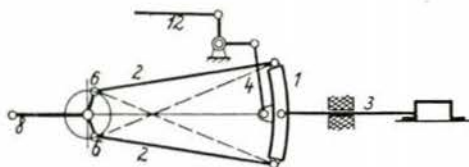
Schemaskizze zu der Stephenson-Steuerung (aus: Henschel-Lokomotiv-Taschenbuch)
